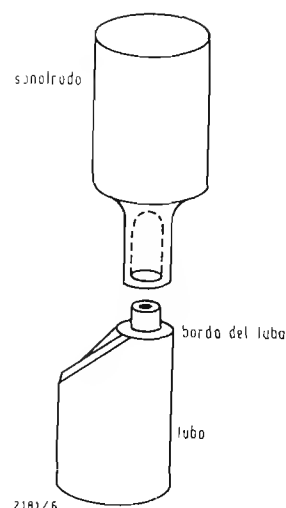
Forma del sonotrodo per la saldatura di un bordo di un contenitore cilindrico al contenitore stesso.
